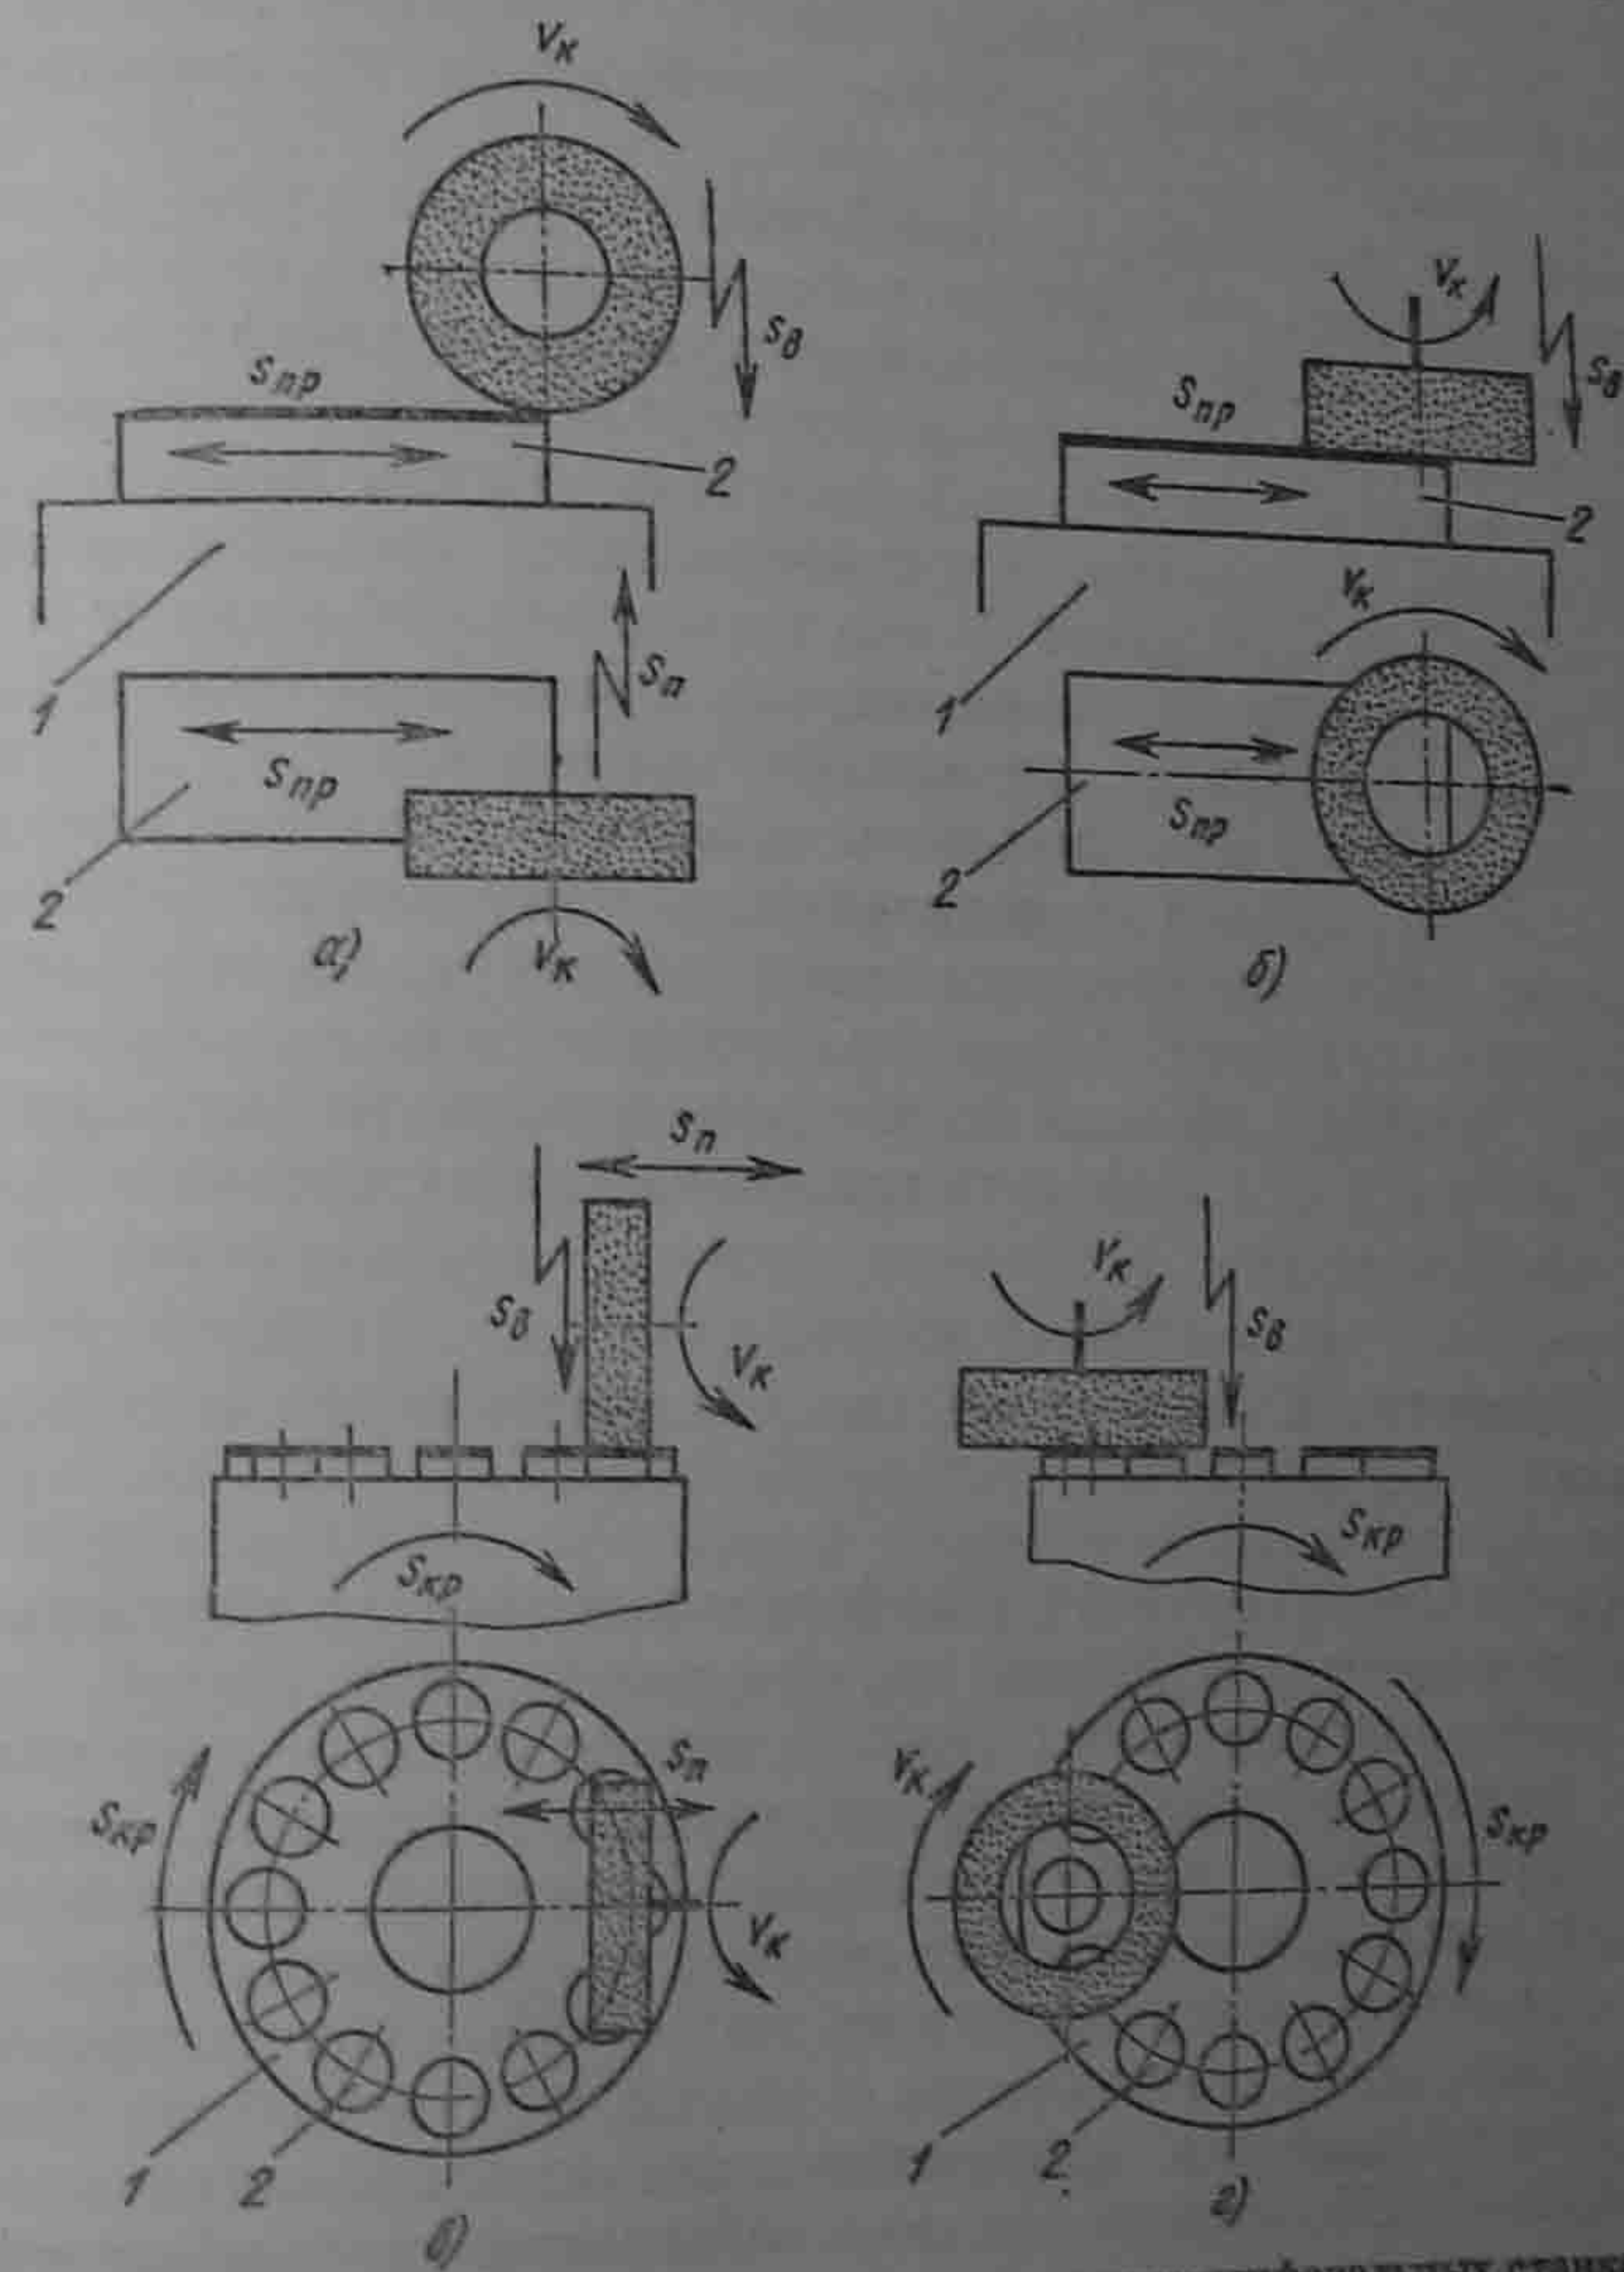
Схема обработки заготовок на плоскошлифовальных станках
